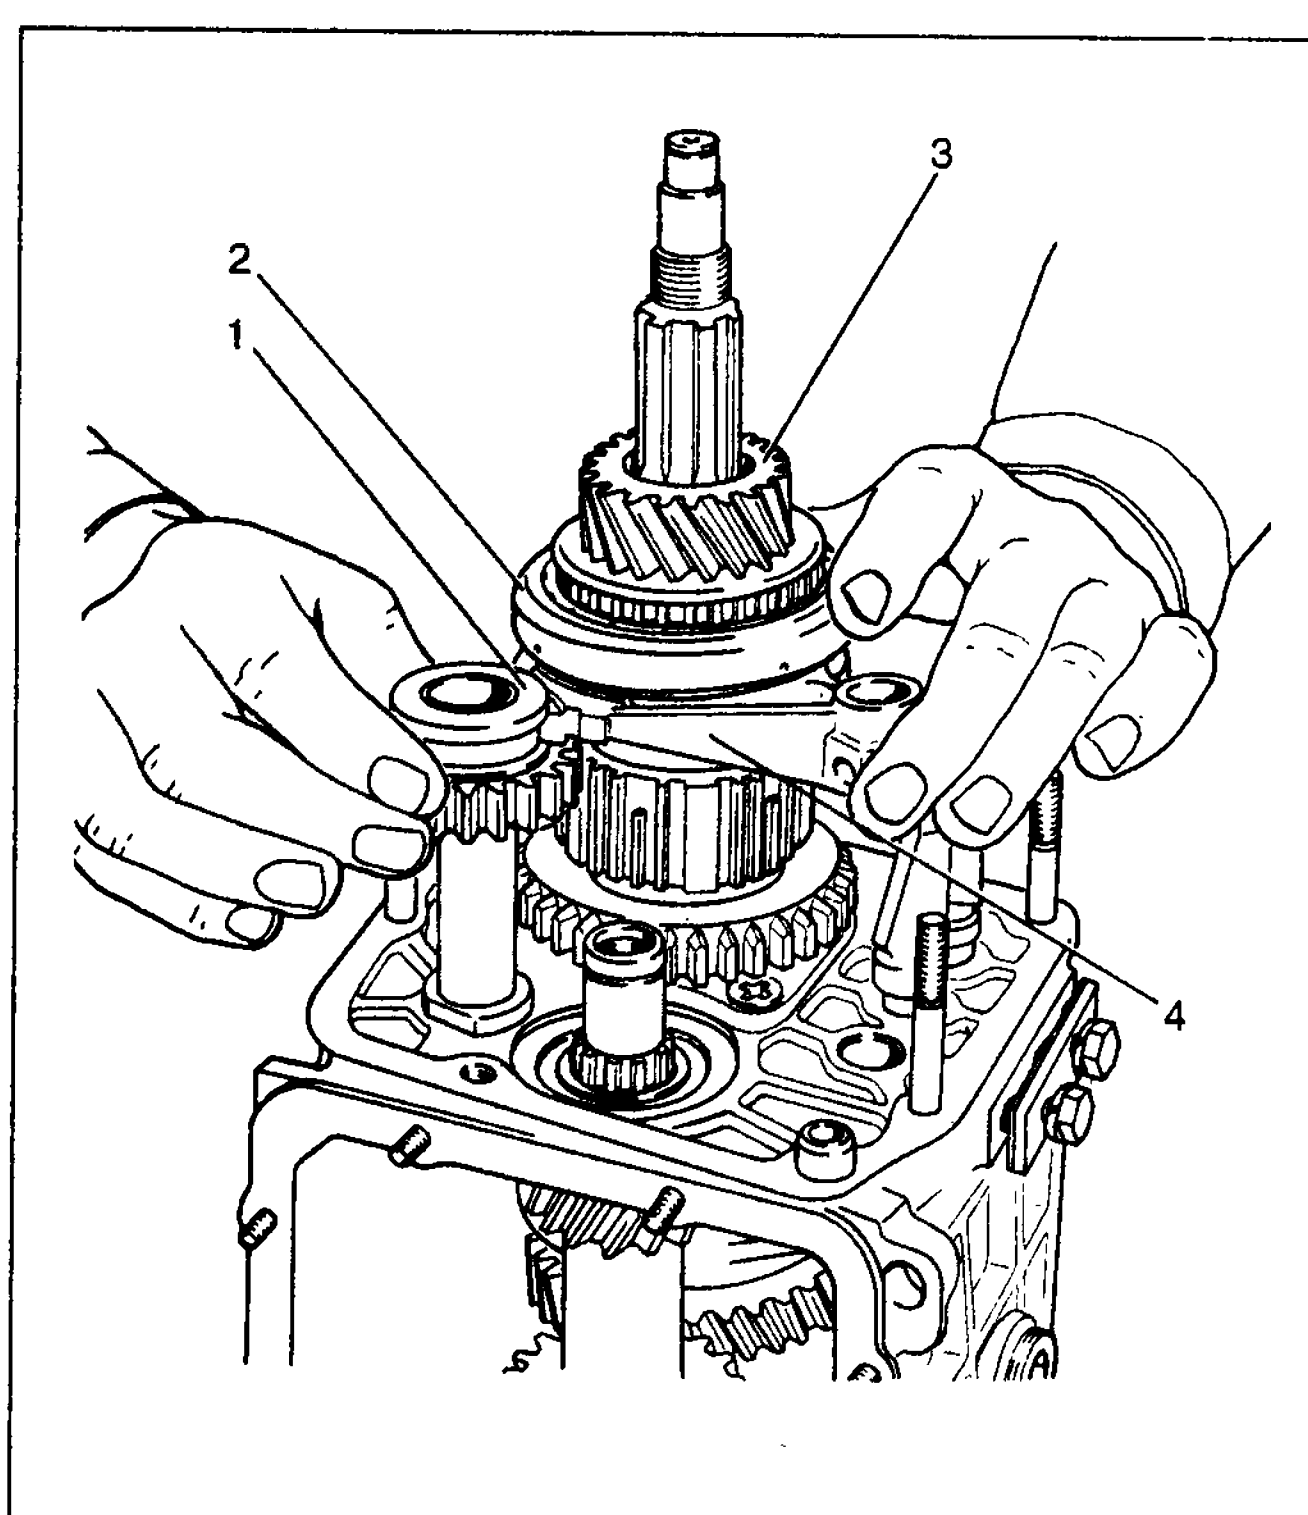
Отвертывание болтов крепления блока шестерен и вилки включения V передачи и заднего хода:
